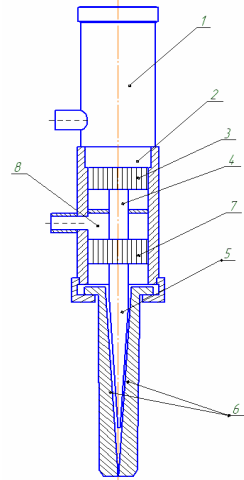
Гидроклиновой ручной инструмент с дополнительным поршнем
